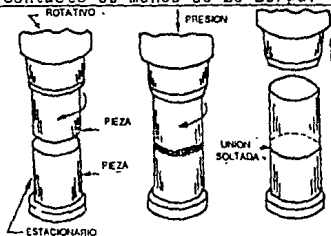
Soldadura por fricción. (Ref. 2).
